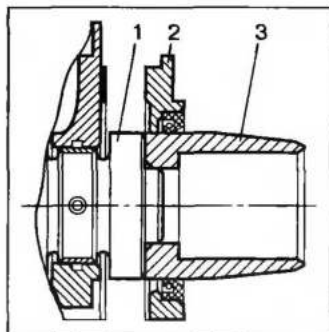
Установка крышки с сальником на задний фланец коленчатого вала: 1 — коленчатый вал; 2 — держатель манжеты; 3 — оправка
